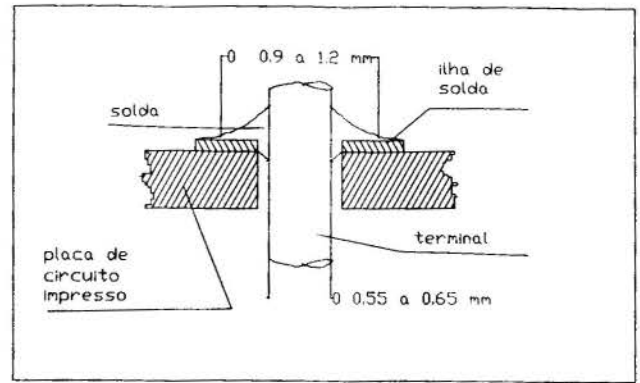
Flutuações de Dimensões na Soldagem Terminal Placa.
